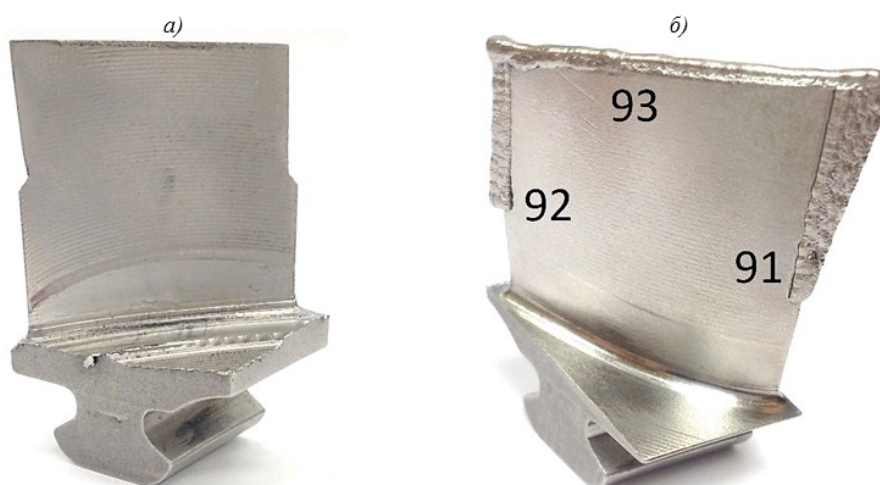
Лопатка компрессора, фрезерованная под наплавку (а) и после процесса лазерной газопорошковой наплавки (б)
